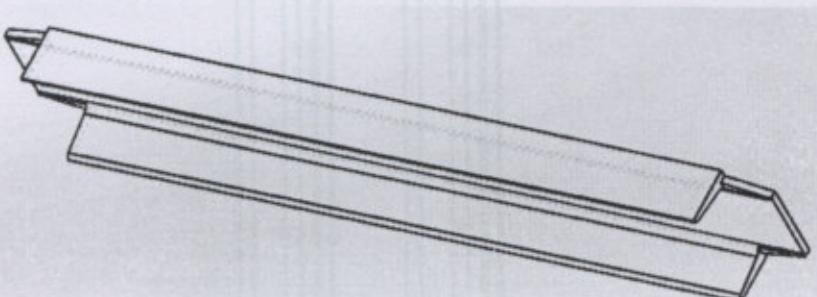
Perfil estructura inferior interior. Plano EE-011.
